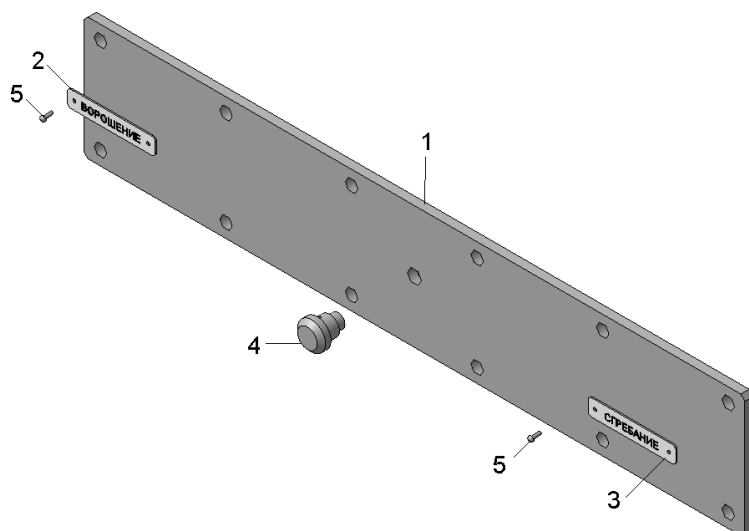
Крышка редуктора УГМ-4,2.04.01.000
